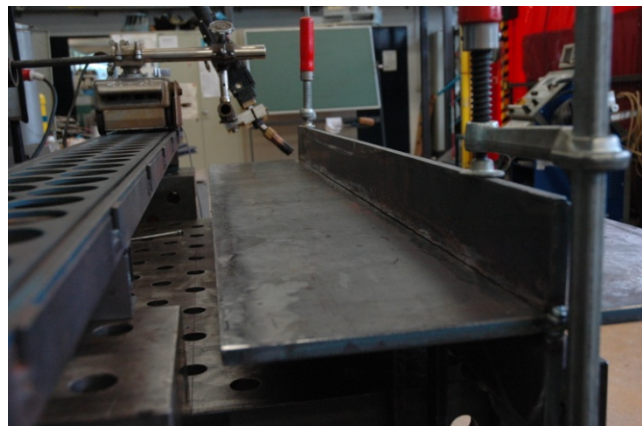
Schweißeinrichtung MAG
